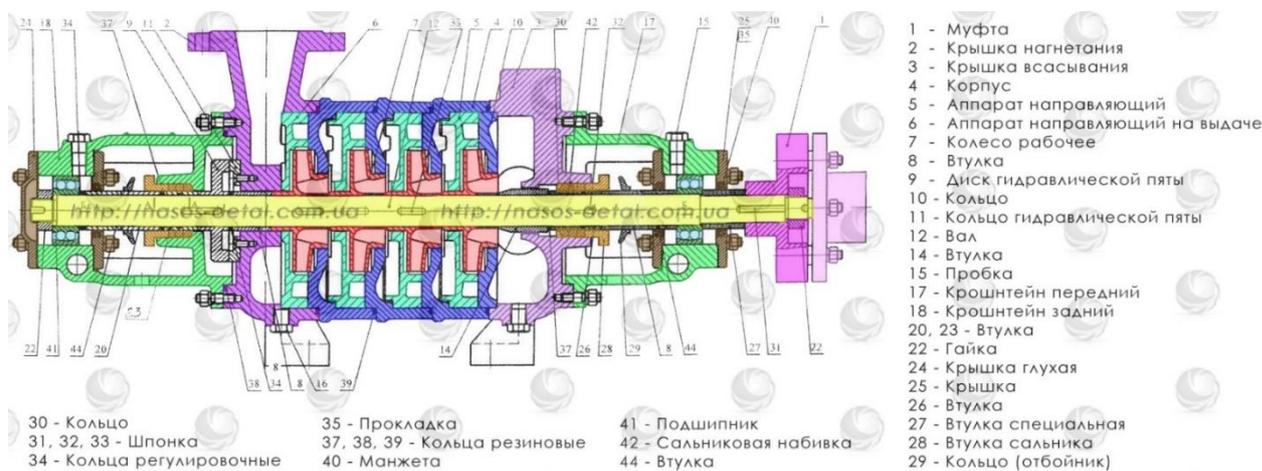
Основные конструктивные элементы насосного агрегата ЦНС-180
